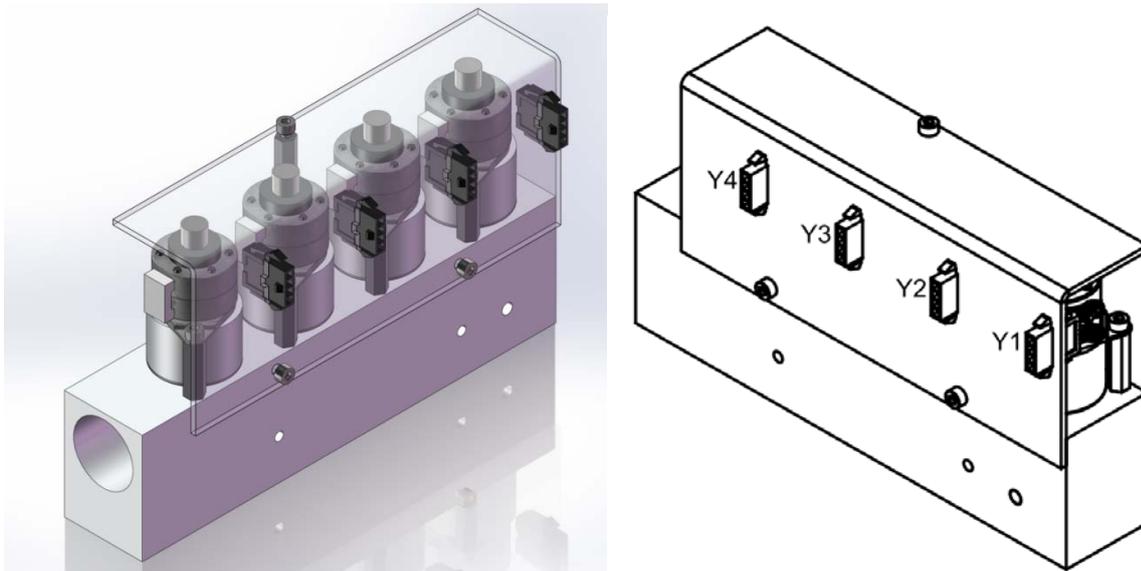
Ventilblock mit 4 Schrittmotor-Ventilen
